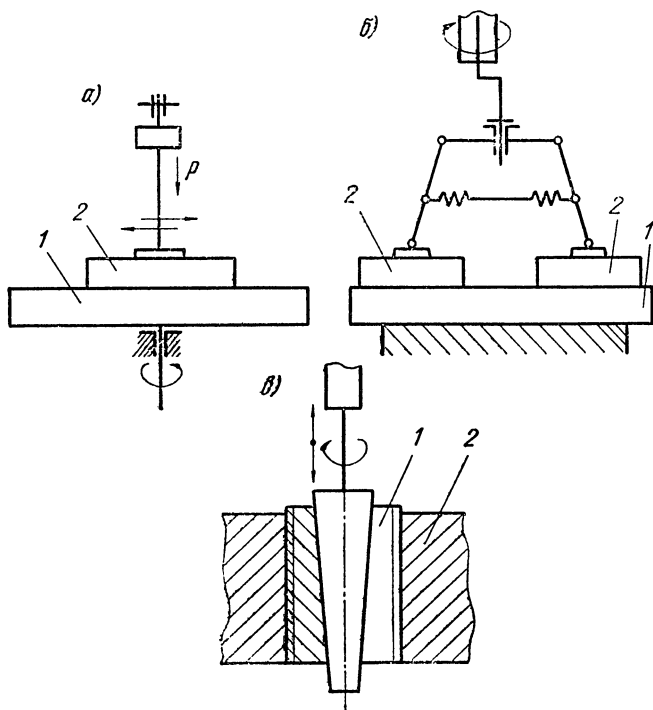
Кинематические схемы устройств для притирки-доводки
